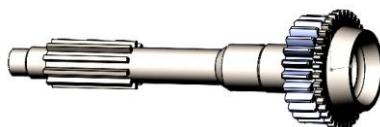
Первинний вал коробки передач автомобіля ГАЗ-24
